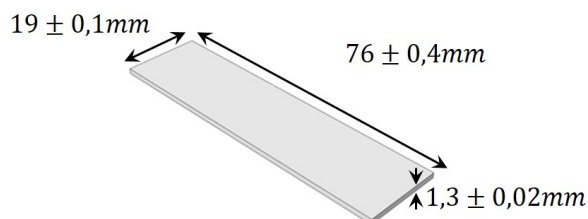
Dimensions d'une éprouvette Almen type A.
